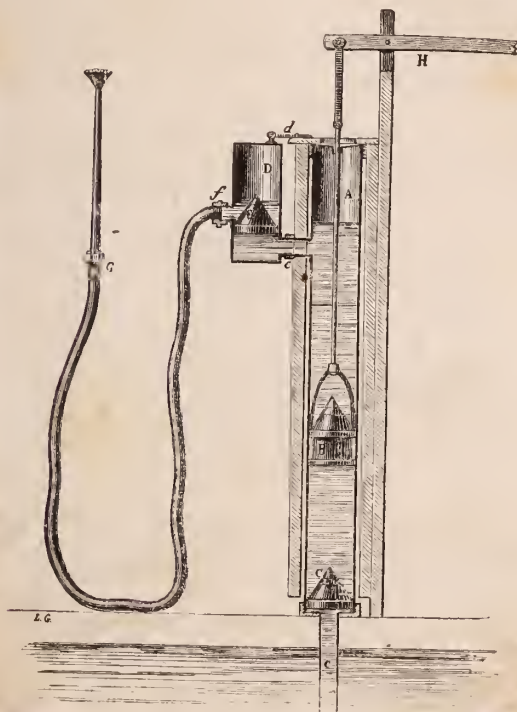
Coupe de la pompe aspirante et foulante de M. Perreaux.
